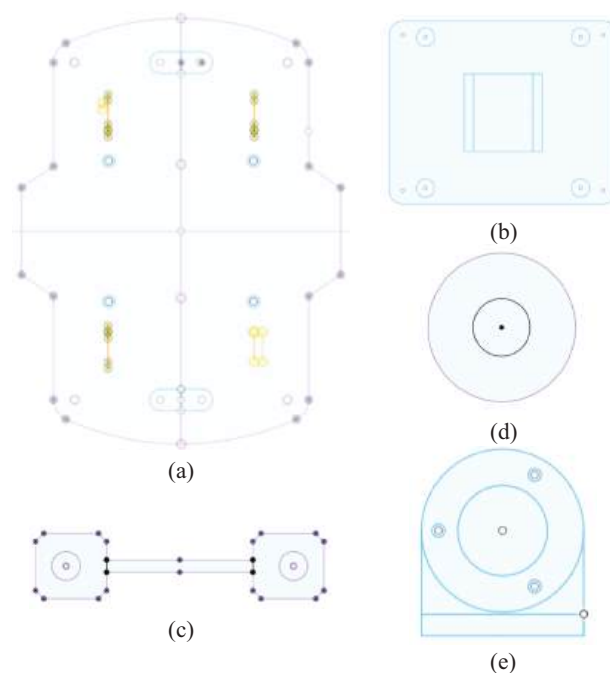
Desenhos das partes em 2D: (a) chassi; (b) base superior; (c) suporte para os rolamentos; (d) eixo; (e) suporte para o encoder.
